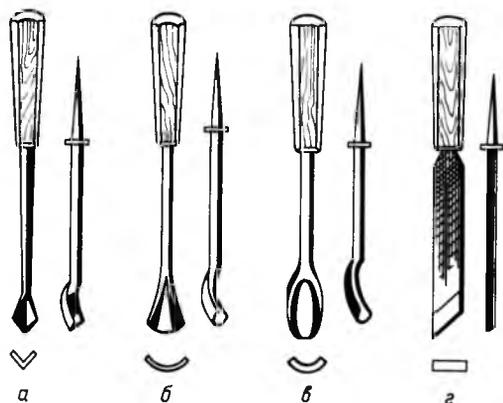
Инструмент (основной) для резьбы по дереву: а — стамески-уголки; б — стамески-клюкарзы; в — стамески-церазики; г — нож-косяк
